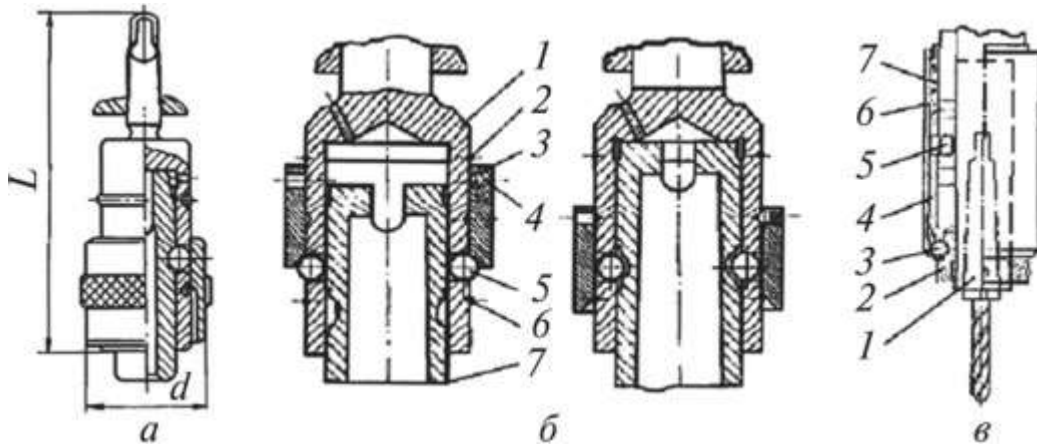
Схема швидкозмінного патрона з кульками для роботи з невеликими зусиллями різання
